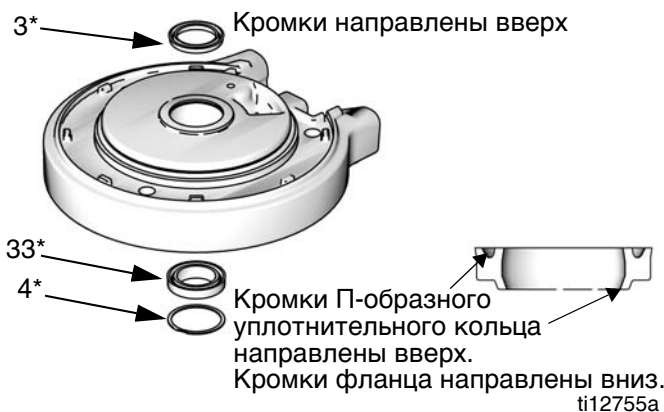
Установка П-образных уплотнительных колец пневматического двигателя
